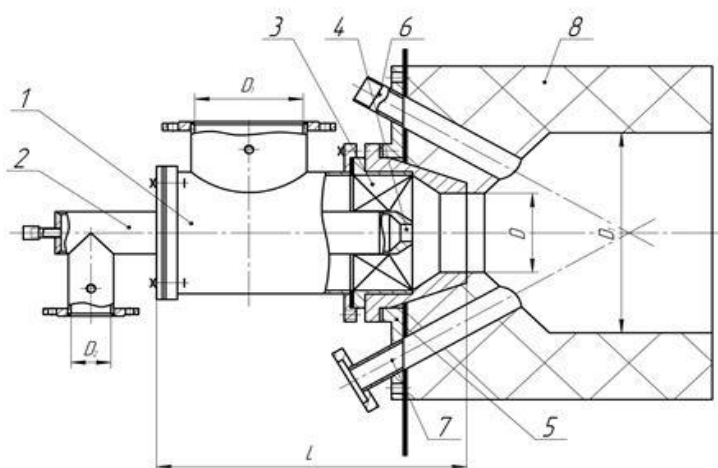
горелка ГНП (модернизированная) 1-воздушный корпус; 2-газовая часть; 3-втулка с лопатками для завихрения воздуха; 4-газовое сопло; 5 – горелочная плита; 6- патрубок для установки запального устройства; 7- патрубок для установки фотодатчика. 8 - горелочный камень
